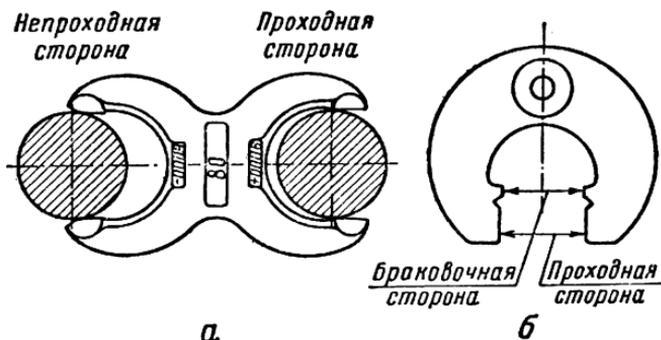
Предельный калибр-скоба для проверки размеров вала:
